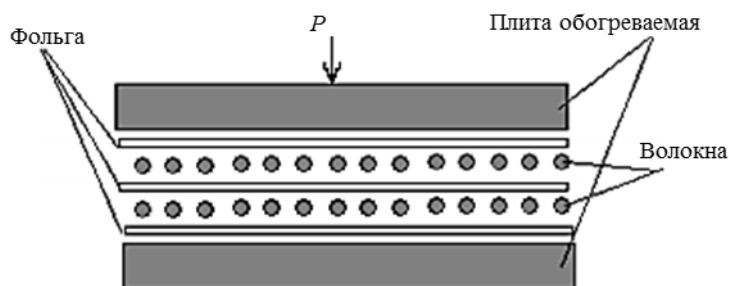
Схема получения металлического композиционного материала (МКМ) с помощью диффузионной сварки
